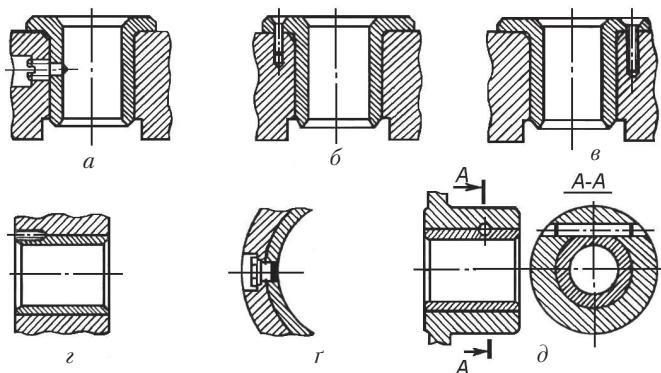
Способи закріплення втулок у корпусі підшипника:
